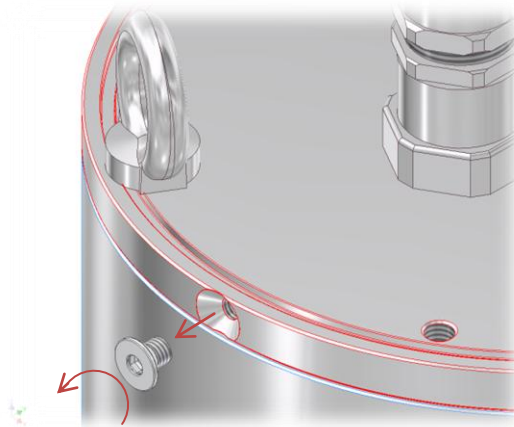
Entfernen der Senkkopfschraube Typ T08-TNXCD
